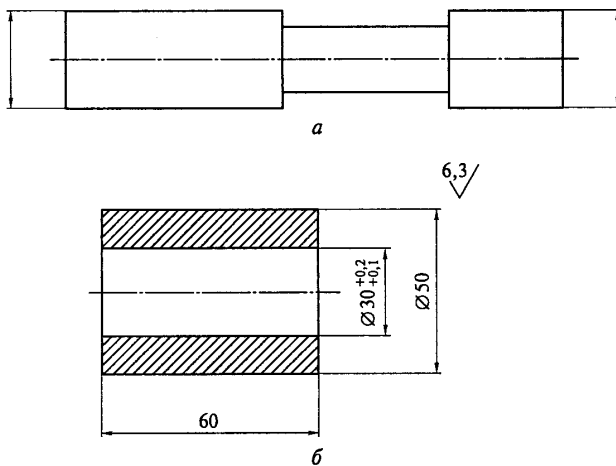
Калибр-пробка (*a*) и контролируемая деталь (*б*)
